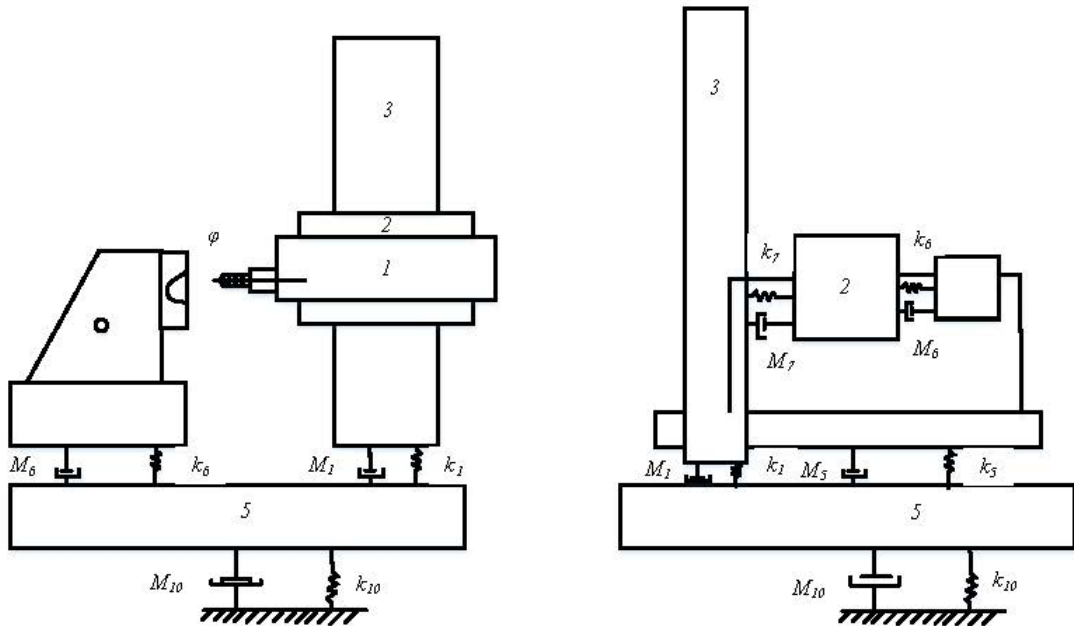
Розрахункова схема дискримінанту динамічної моделі фрезерного верстата
